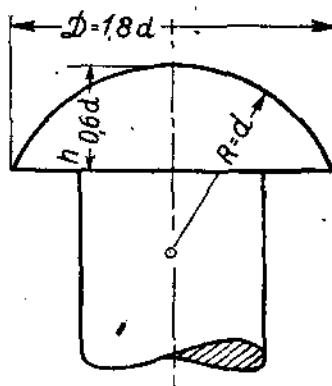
Форма замыкающей головки прочно - плотного шва.
